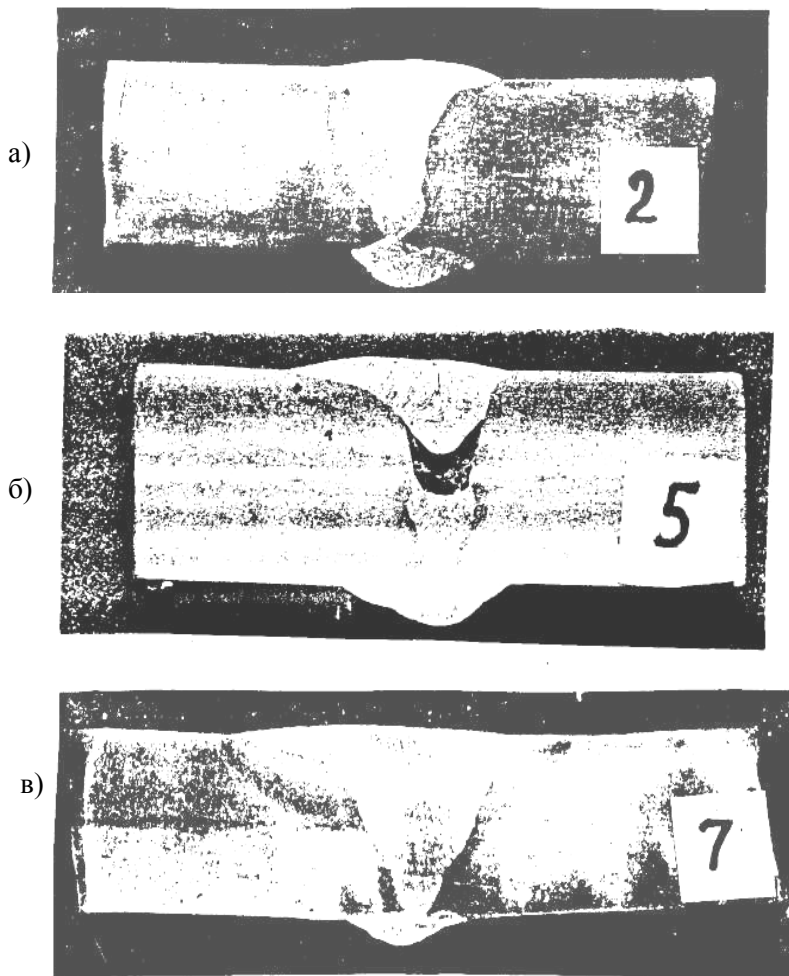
Макрошлифы сварных соединений, выполненных с применением дополнительной проволоки: а) угол раскрытия кромок 30° и 60° Сила тока 670-720А, напряжение на дуге 48-50В, скорость сварки 20м/час; б) то же, скорость сварки 17м.ч.; в) угол раскрытия кромок 80° и 90° тока 670-720А, напряжение на дуге 48-50В, скорость сварки 17 м/час
